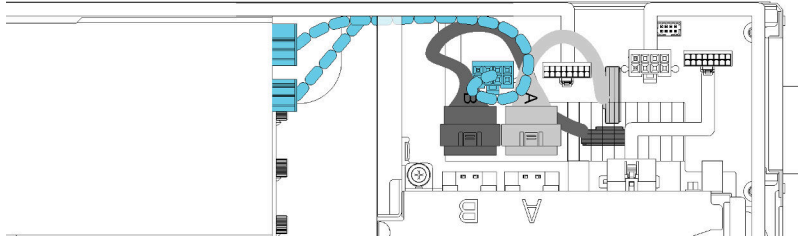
Disposición del cable de alimentación auxiliar de expansión frontal para el nodo de expansión
